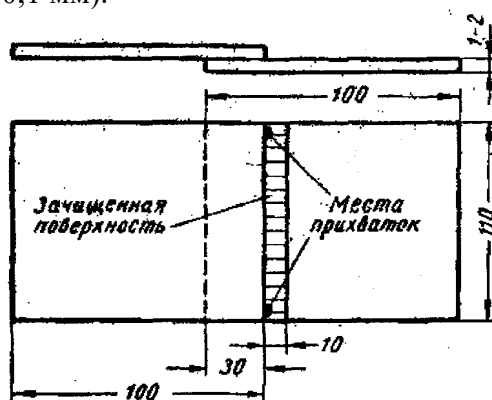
Схема сборки и прихватки пластин перед пайкой
